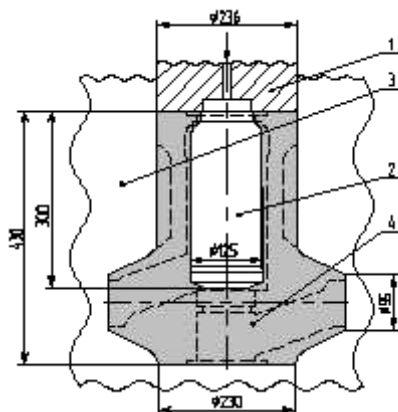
Схема штамповки корпуса типа тройника из стали 12Х18Н10Т:
